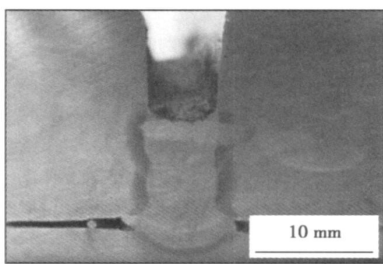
焊剂带约束电弧超窄间隙焊缝形貌
